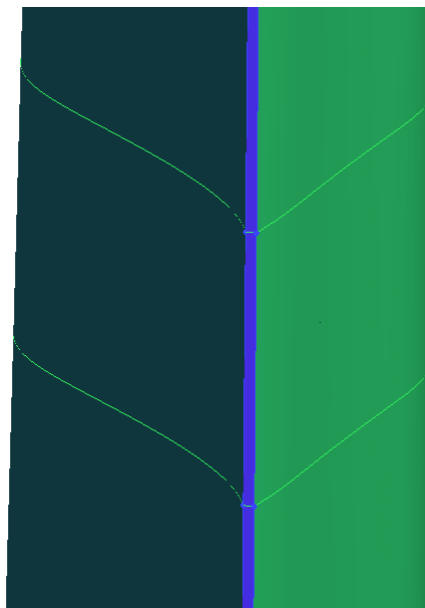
Detalhe do bordo de fuga plano aproximado.
